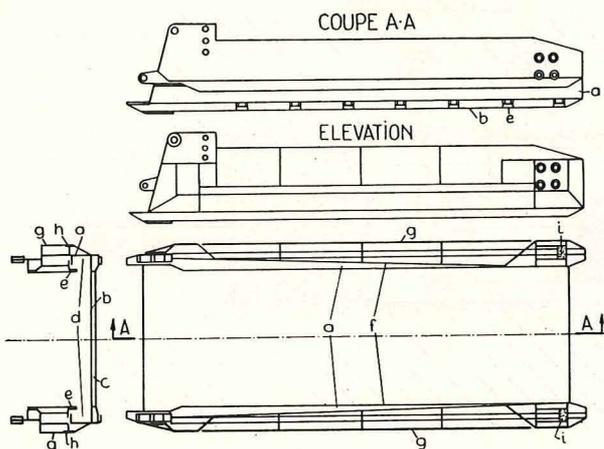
Coupe, élévation et vue en plan de l'accumulateur.
